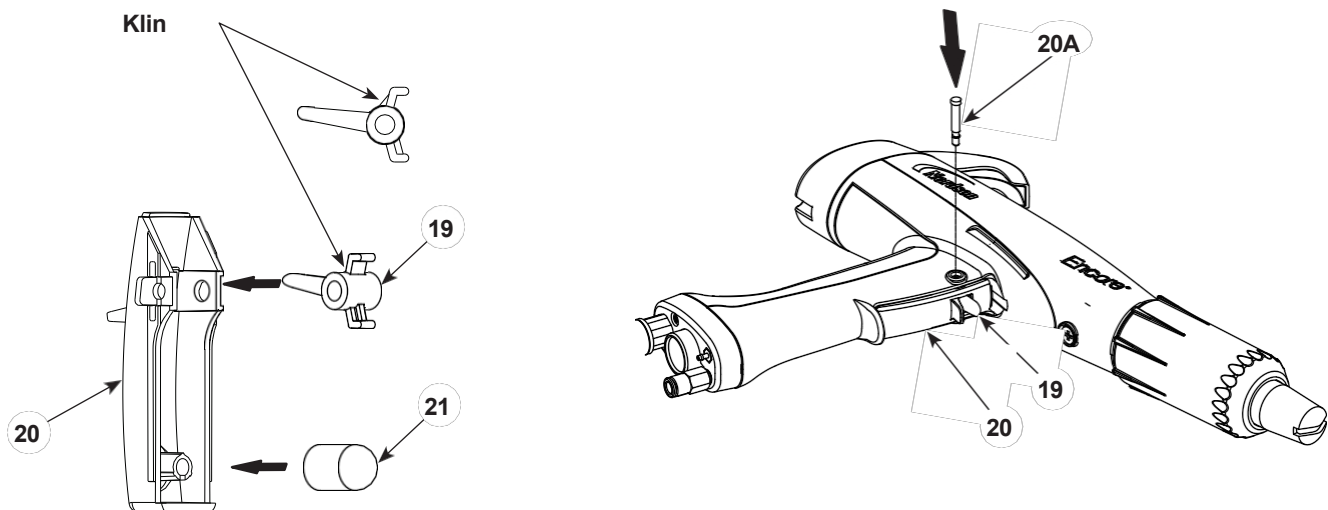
Instalacja przełącznika wyzwalania– Krok 3
